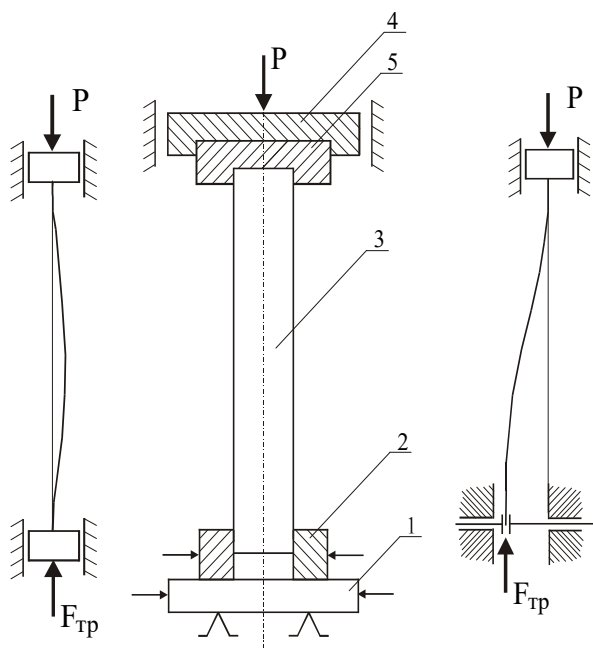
Способ установки и закрепления деталей при запрессовке (стол и втулка могут иметь горизонтальные перемещения): 1 – стол; 2 – втулка; 3 – вал; 4 – пуансон прессы; 5 – закрепительная втулка
